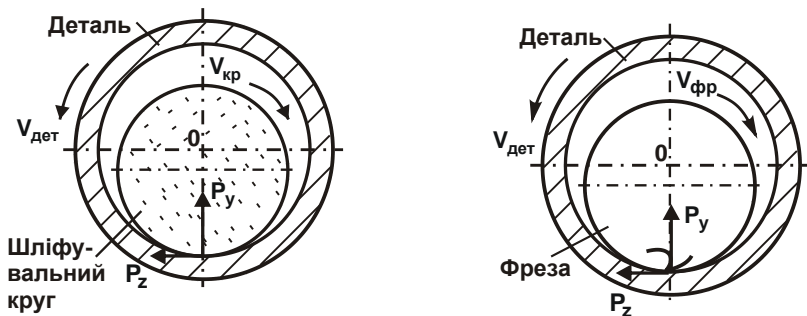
Розрахункові схеми шліфування (а) і фрезерування (б) отвору
